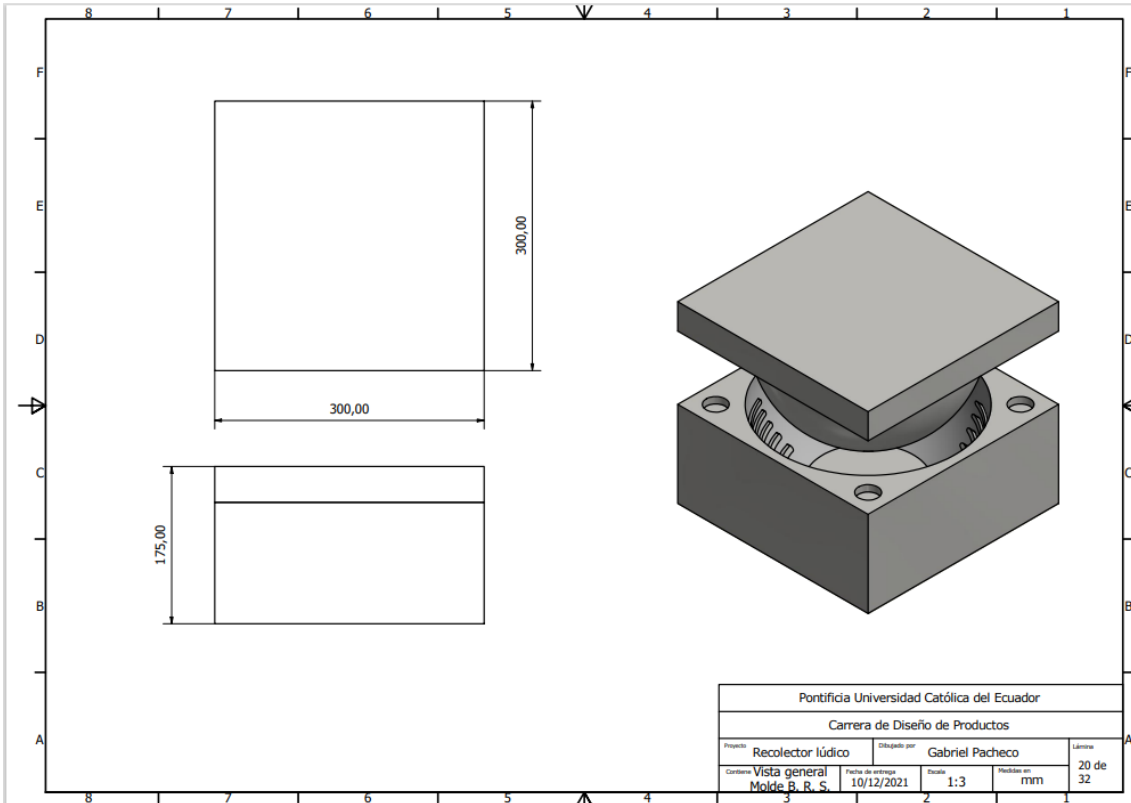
Segundo molde bolsa de caucho superior, elaborado por el autor
